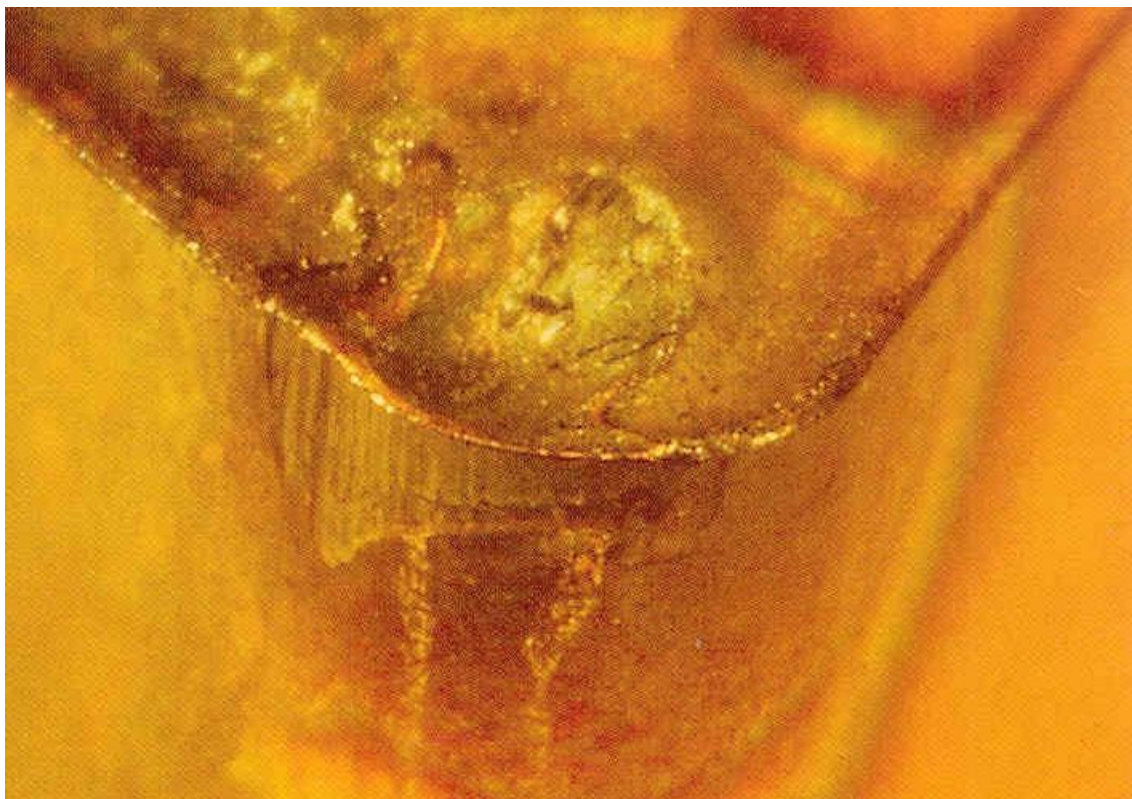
Herramienta con desgaste de cráter en cara de desprendimiento [79].
